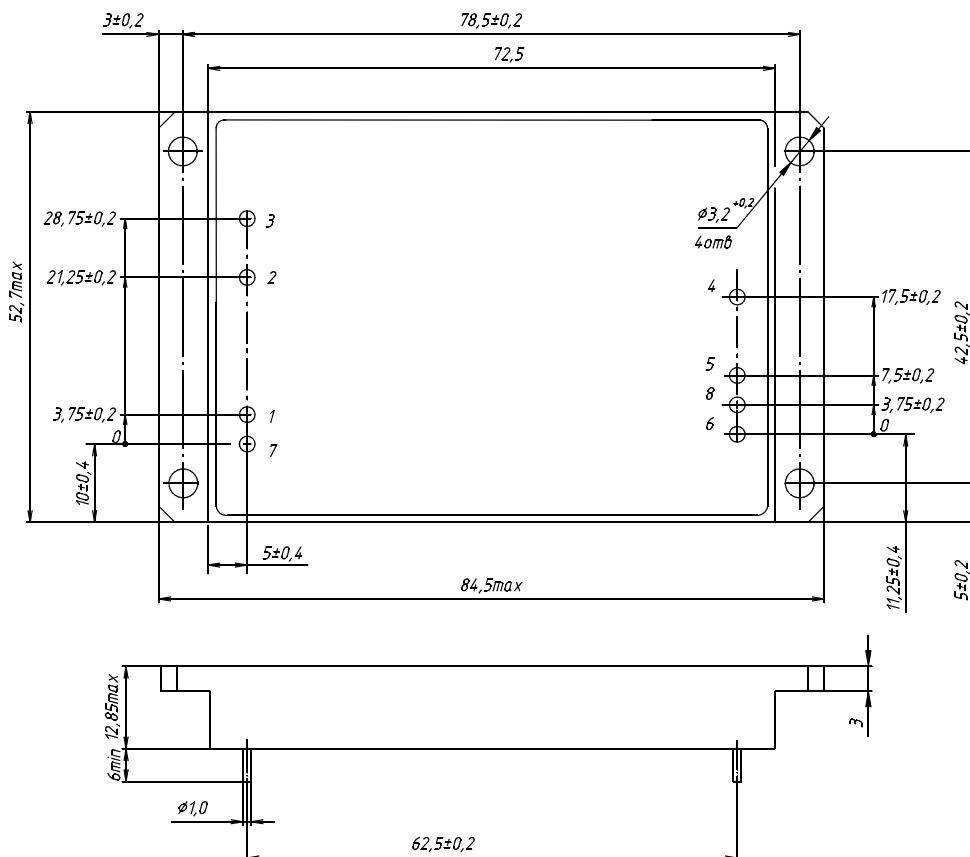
Модуль одноканальный в корпусе с фланцами (индекс «У»).
